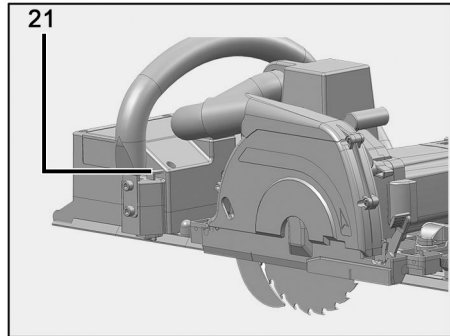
Prolongar el corte longitudinal con el tope de desplazamiento
